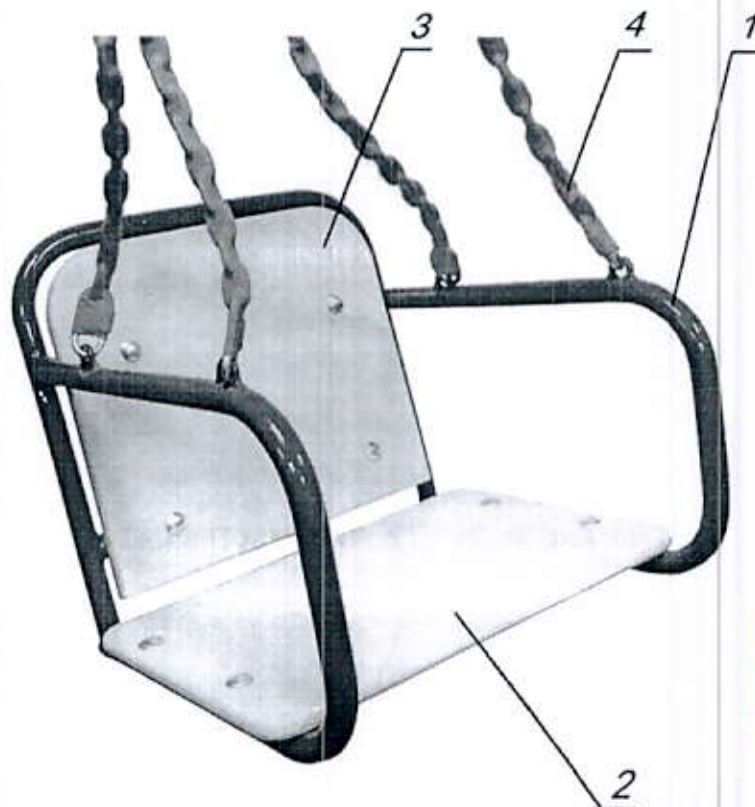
Общий вид Подвески со спинкой для качелей РТР 019.3
